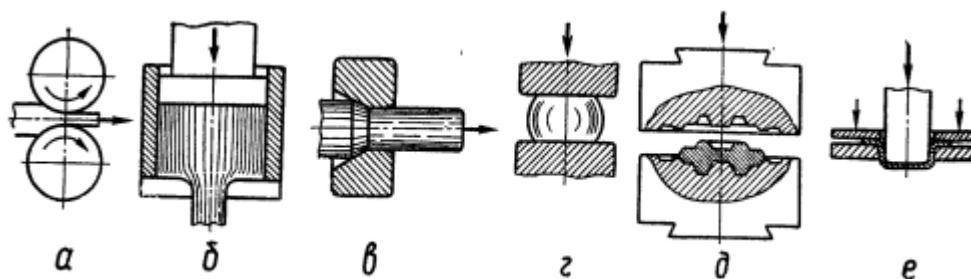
Схемы основных видов обработки металлов давлением: а - прокатка, б - прессование, в - волочение, г - ковка, д - объёмная штамповка, е - листовая штамповка
